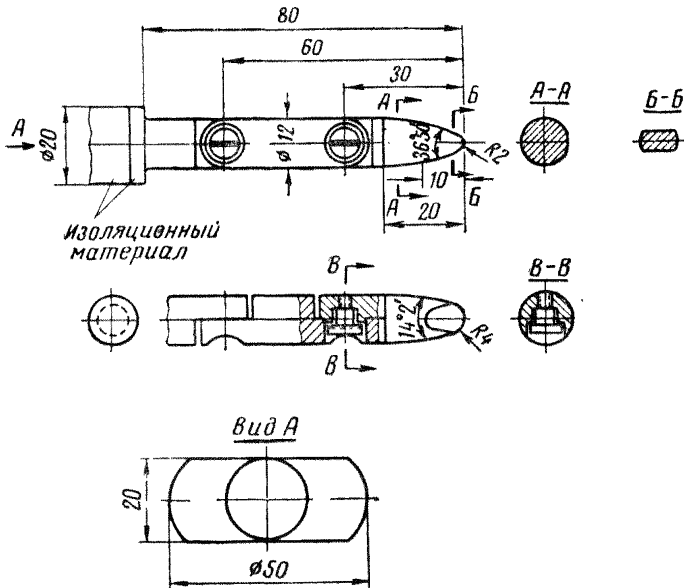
Стандартный испытательный палец, размеры в миллиметрах.
